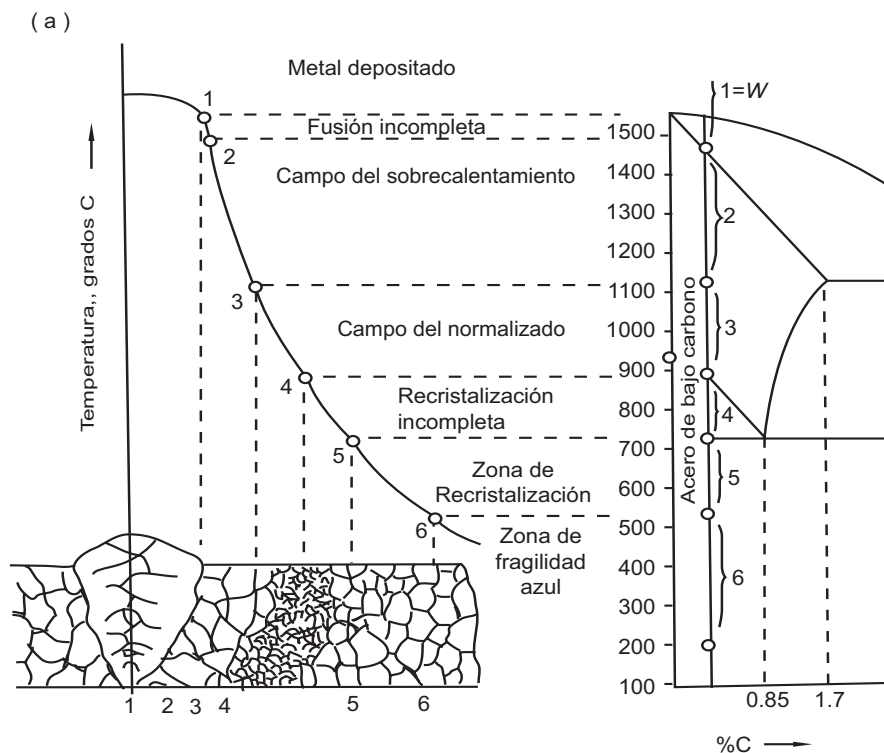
Solidificación progresiva del metal fundido en un depósito de soldadura [12]
